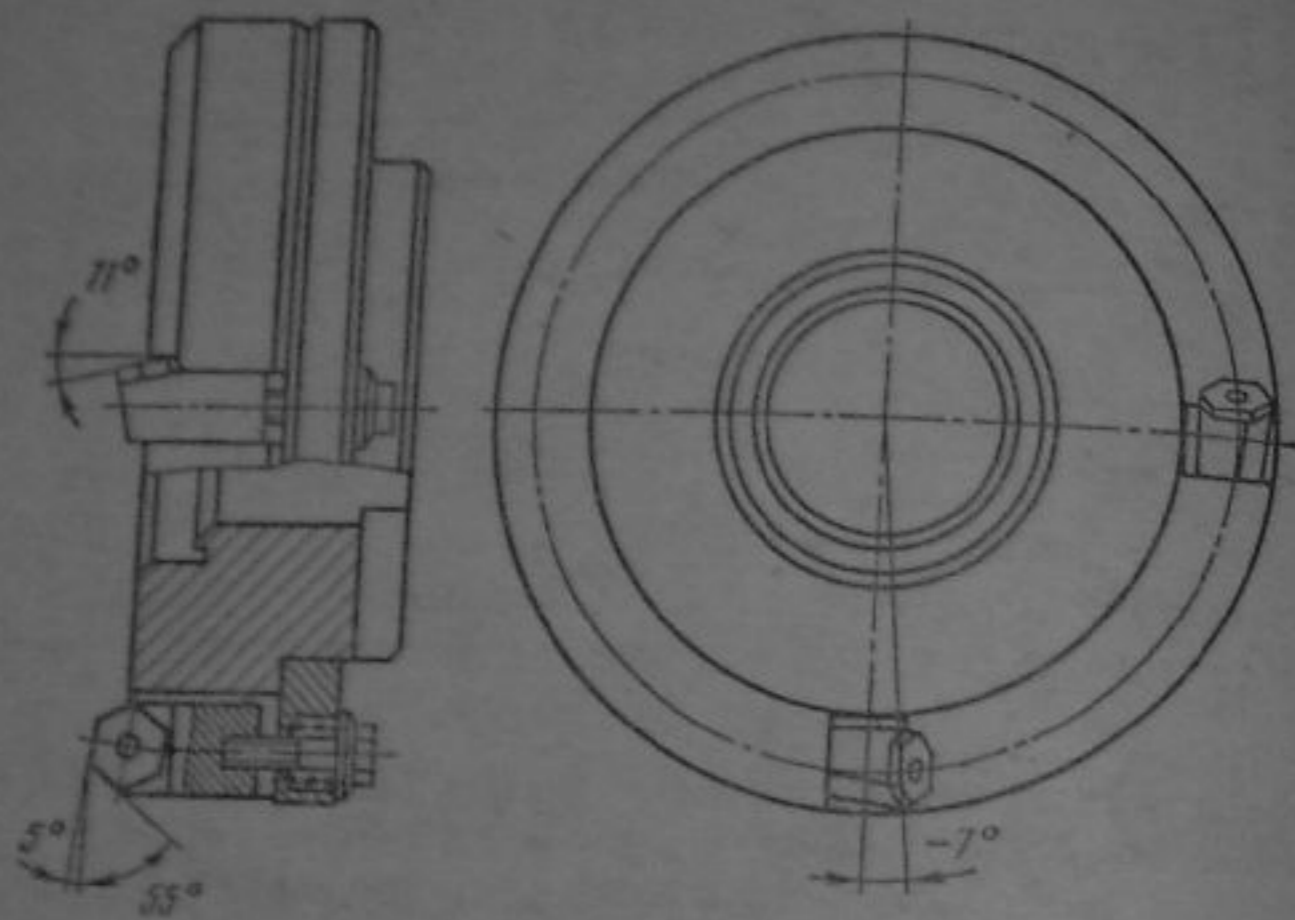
Фреза сборная торцовая с механическим креплением шестигранных неперетачиваемых пластин из твердого сплава
